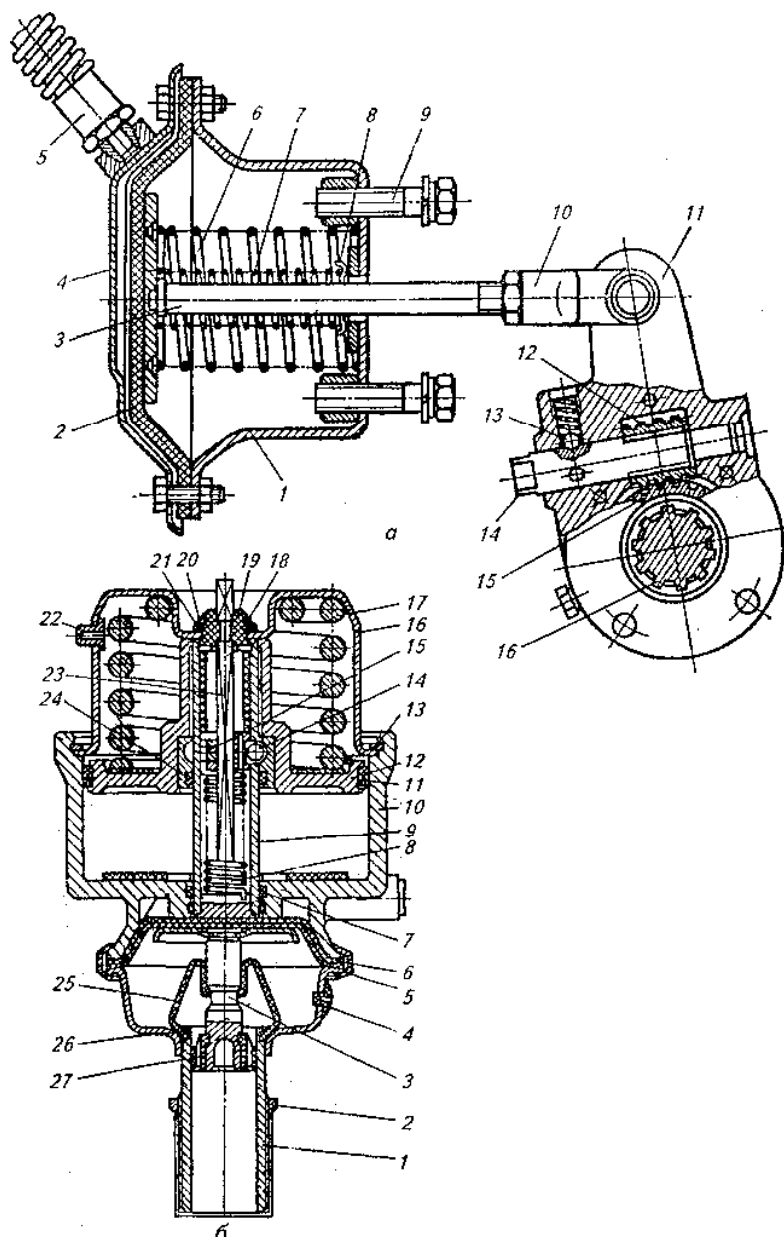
Тормозные камеры: а — мембранная: 1— корпус камеры; 2 — диафрагма; 3 — шток; 4 — крышка корпуса; 5 —гибкий шланг; 6, 7—пружины; 8— уплотнительная шайба; 9—болт; 10— вилка
